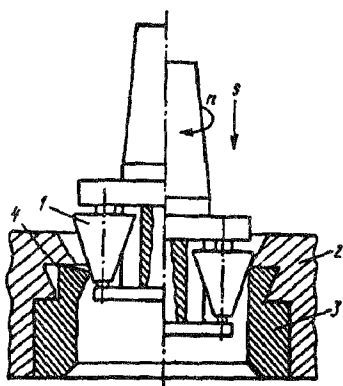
Схема сборки клапанного седла вальцеванием
